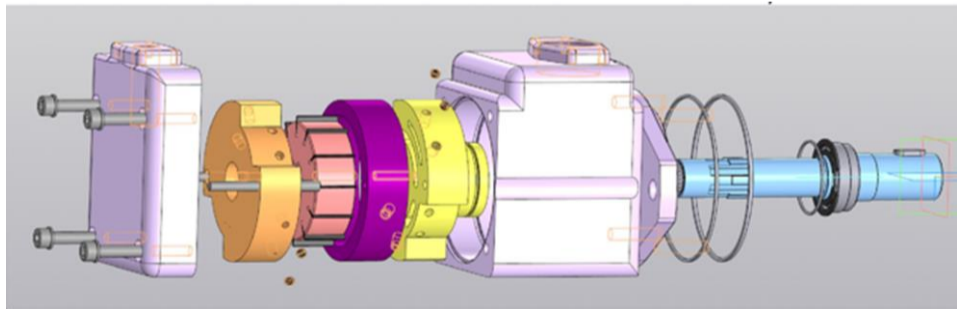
3D модель пластинчатого насоса Bosch PVV
